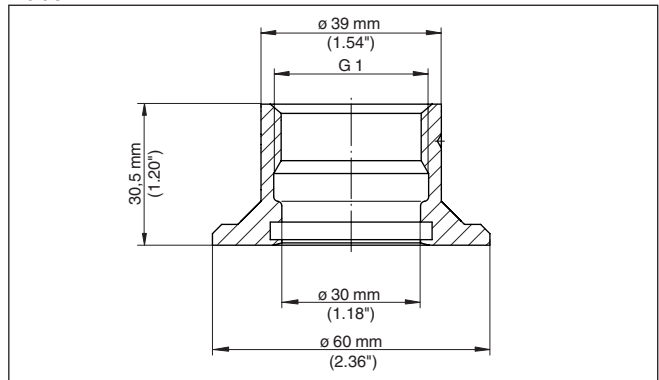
Maße Einschweißstutzen G1 (DIN 3852-X) - lebensmittelgeeignet
